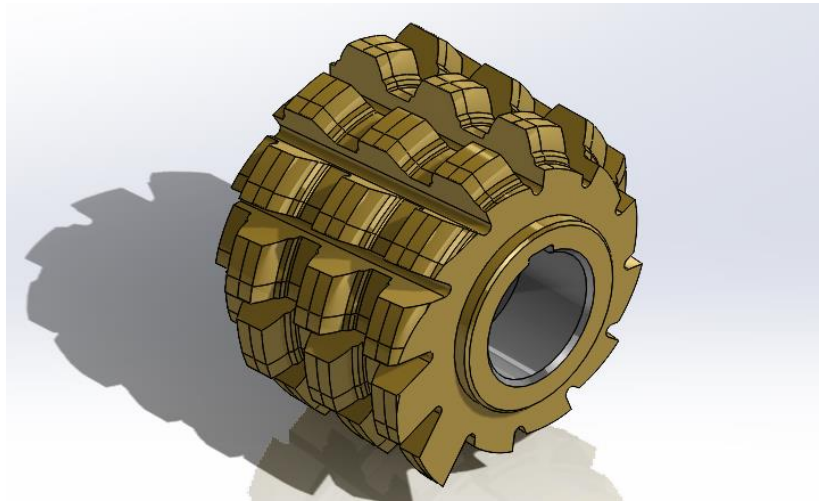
Імпортована модель черв'ячної фрези
